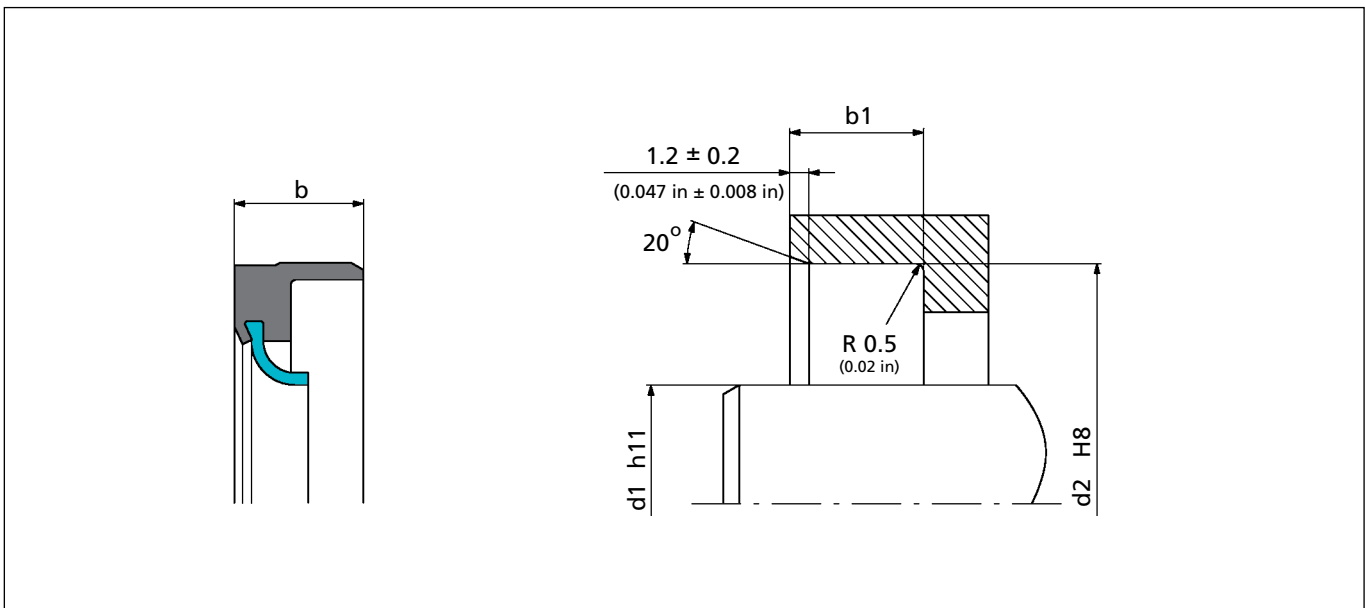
Einbauzeichnung für Drücke bis zu 0,5 MPa (73 psi)
